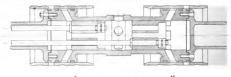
Doppelkolbensteuerung mit innerem Einlafs, ausgeführt von der Duisburger Maschinenbau-Actiongesellschalt, Duisburg.
